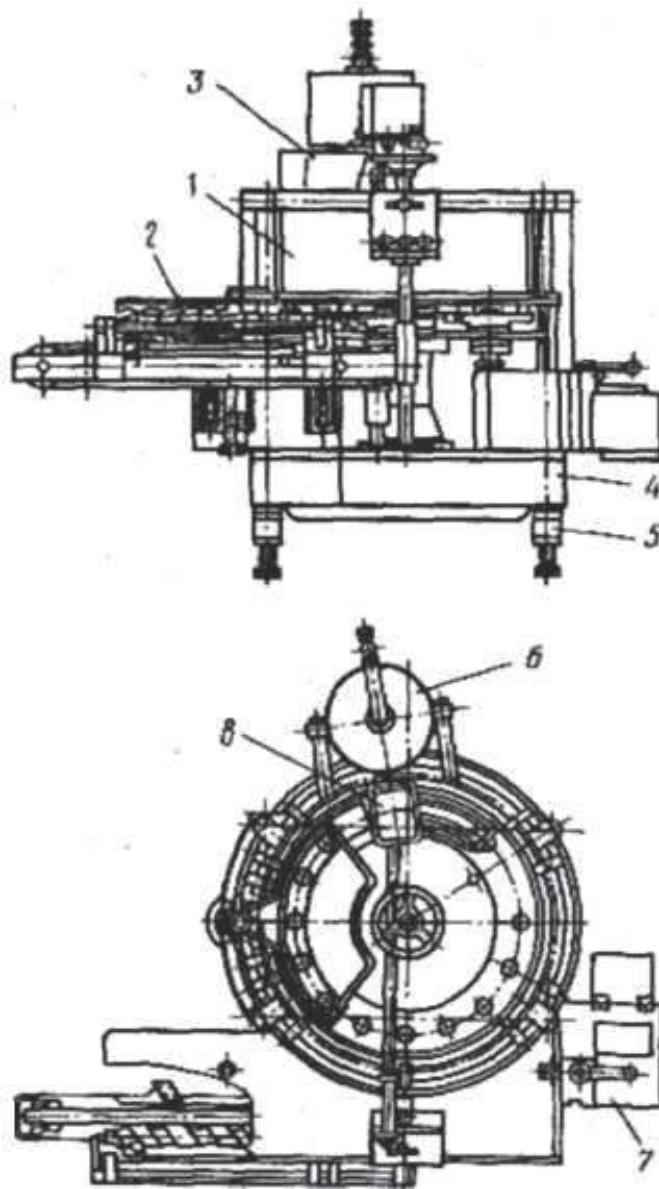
Автомат Б4-КДН-16: 1-карусель; 2-пристрій живлення; 3-бункер для горошку; 4-станина; 5-опора; 6-бак для заливок; 7-привід; 8-бункер для заливки.
